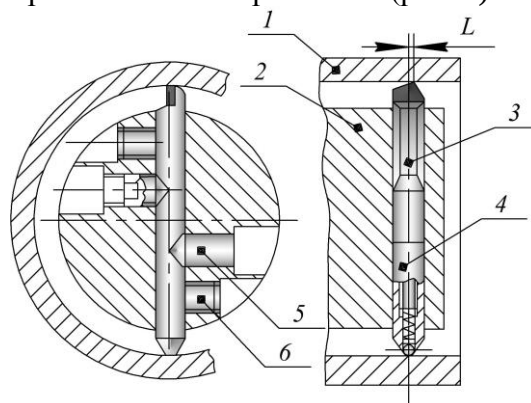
Конструкция инструмента для совмещенной обработки отверстий тонким растачиванием и пластическим деформированием: 1– обрабатываемая деталь; 2– борштанга; 3– резец; 4– шариковый раскатник; 5– винт регулировочный; 6– винт зажимной
